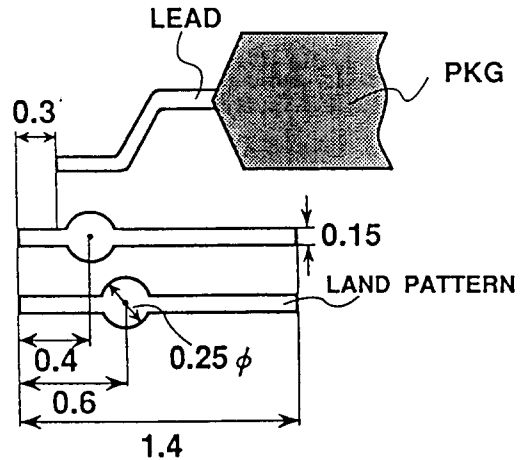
Projected Solder Pre-coat를 위한 0.3mm Pitch Land Pattern Design
